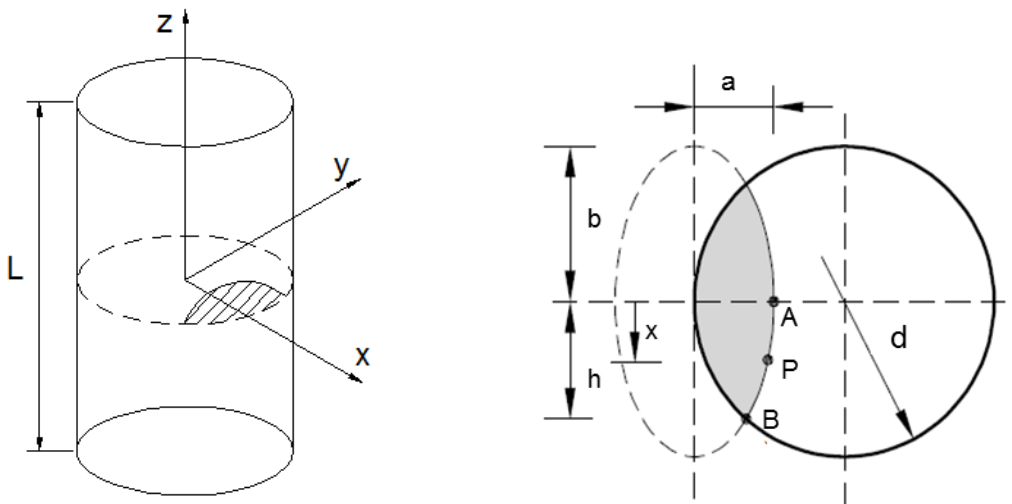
Cilindro fisurado y esquema de la sección transversal con una fisura semielíptica.
